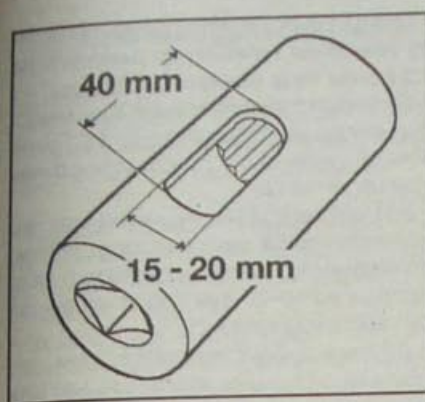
Размеры приспособления Renault Mot. 997 для снятия корпуса форсунки с двигателя G8T 714
